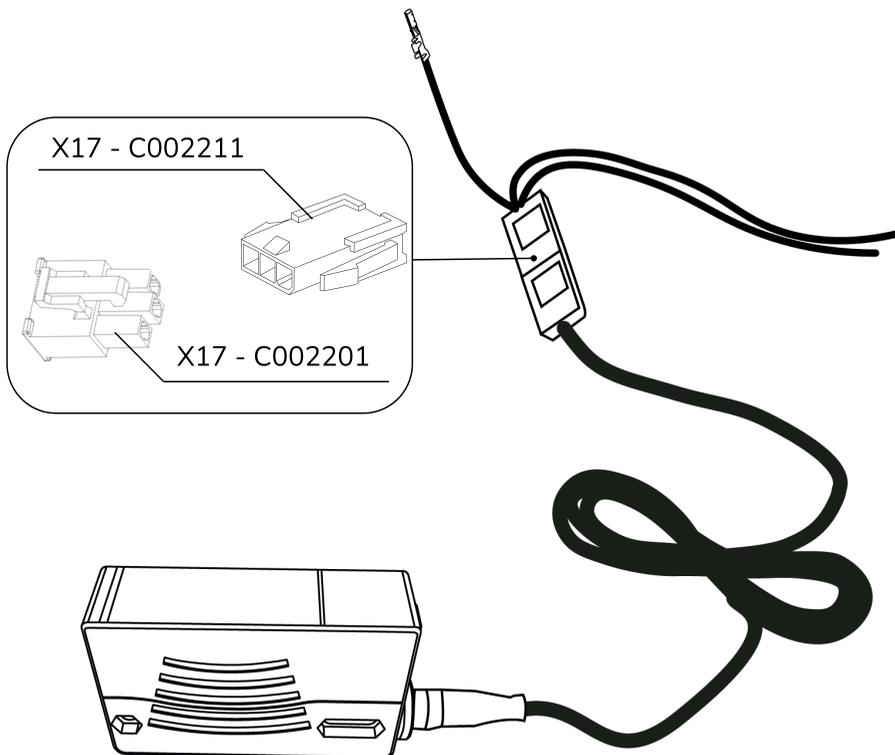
Predisposizione KiwiRoof per collegamento a Key
